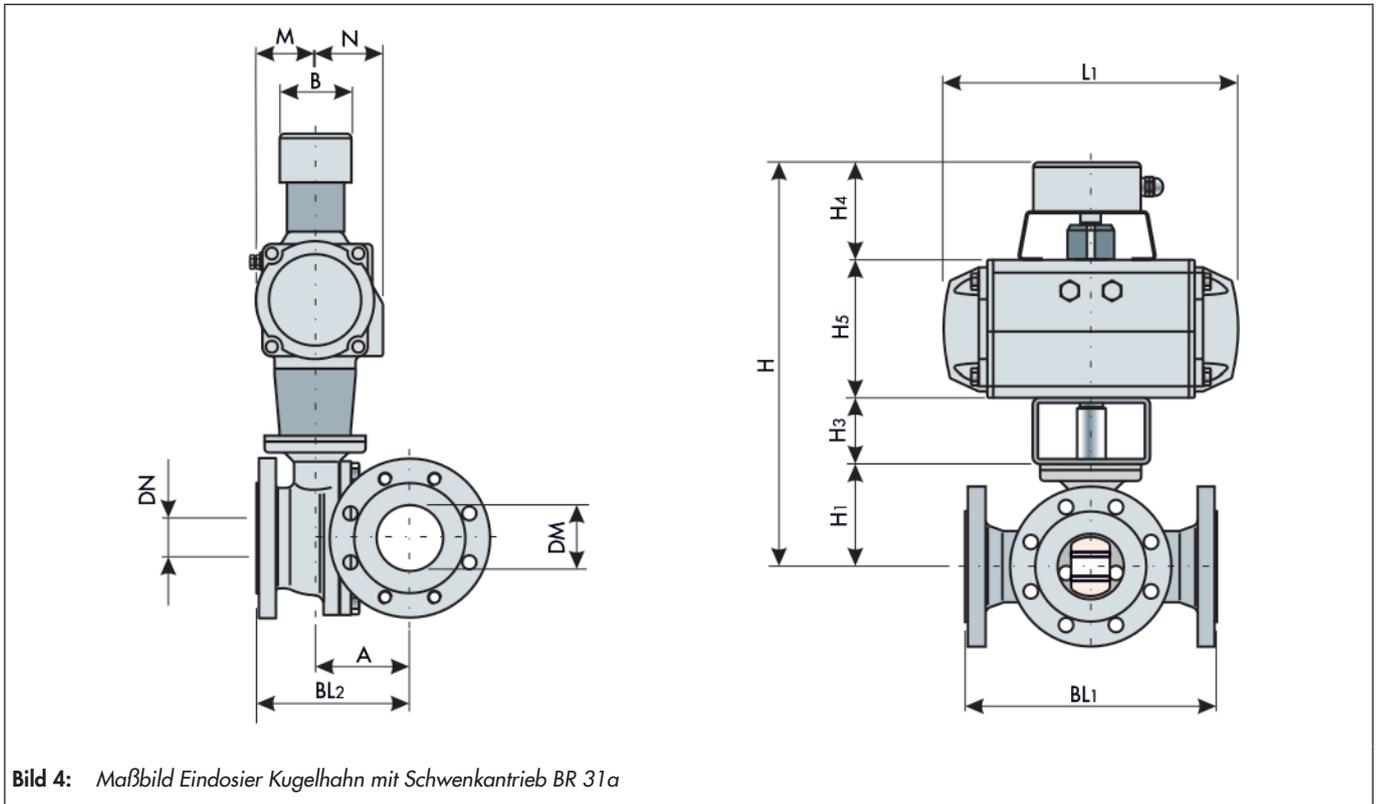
Maßbild Eindsier Kugelhahn mit Schwenkantrieb BR 31a
